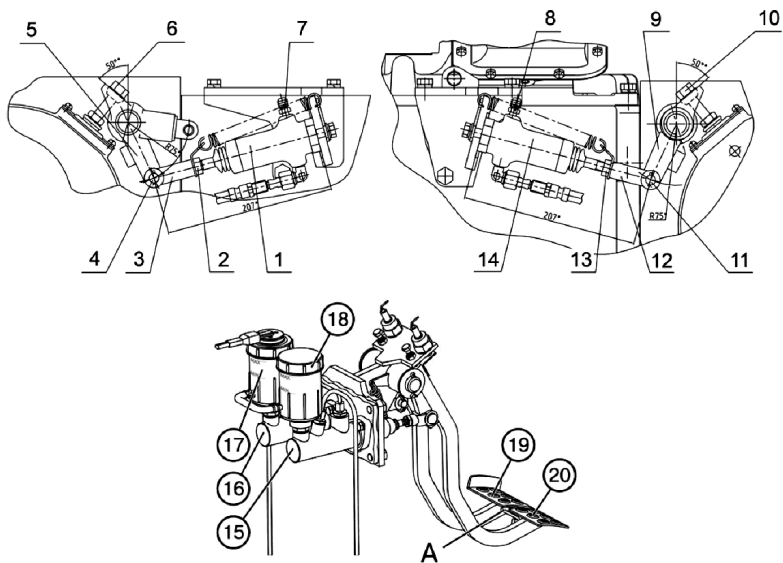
Регулировка длины рабочих цилиндров: 1, 14 – рабочие цилиндры; 2, 13 – контргайки; 3, 12 – вилки; 4, 11 – пальцы; 5, 9 – рычаги; 6, 10 – болты-тяги; 7, 8 – перепускные клапана; 15, 16 – главные тормозные цилиндры; 17, 18 – бачки; 19, 20 – педали
